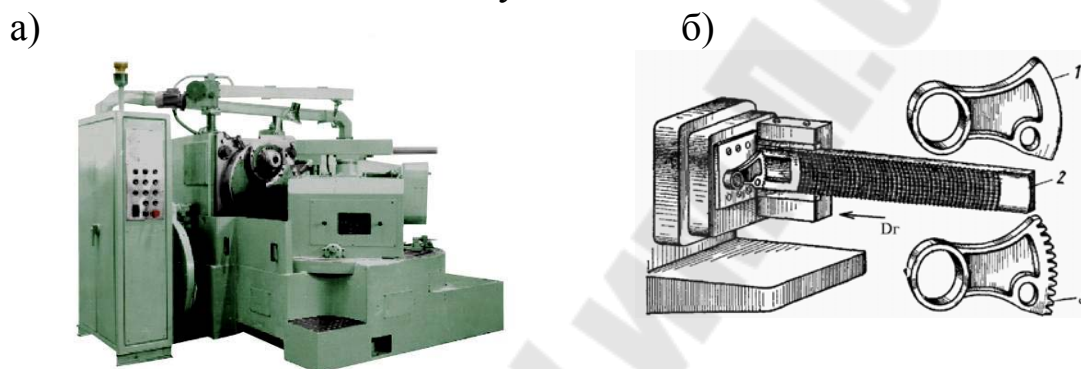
Общий вид зубопротяжного станка (а) и схема обработки зубчатого сектора(б)
